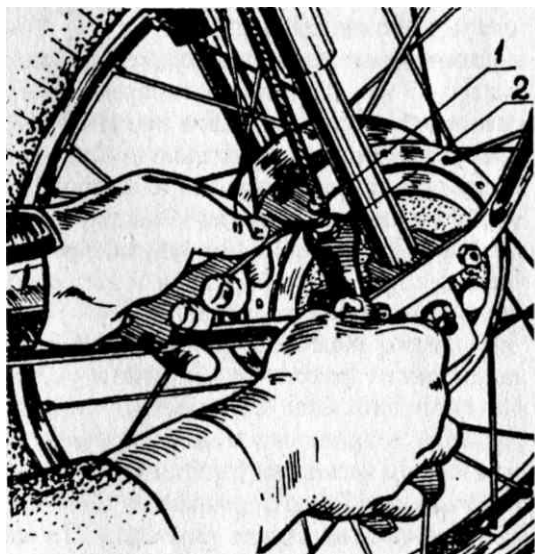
Регулировка тормоза переднего колеса: 1 - упор; 2 - гайка
